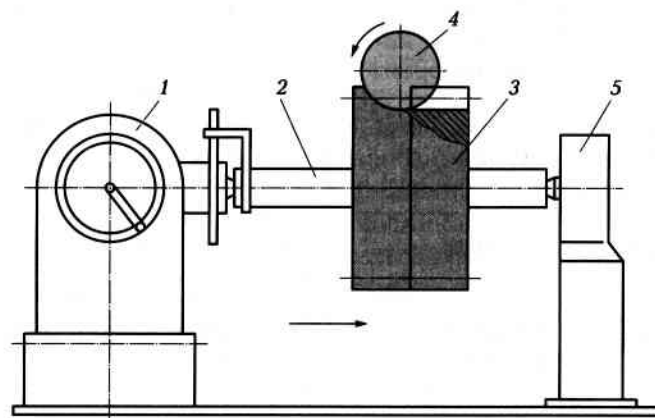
Схема нарезания цилиндрического зубчатого колеса методом копирования:
